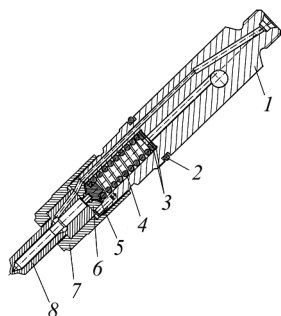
Форсунка: 1 – корпус форсунки; 2 – кольцо уплотнительное; 3 – шайба регулировочная; 4 – пружина; 5 – штанга форсунки; 6 – проставка; 7 – гайка распылителя; 8 – распылитель
